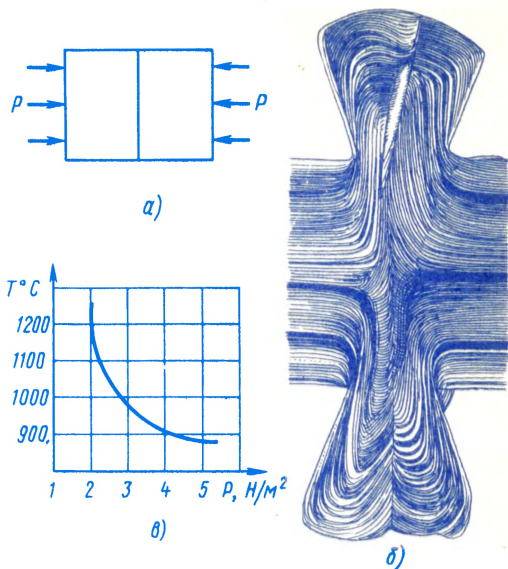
Соединение деталей сваркой давлением без внешнего нагрева:
